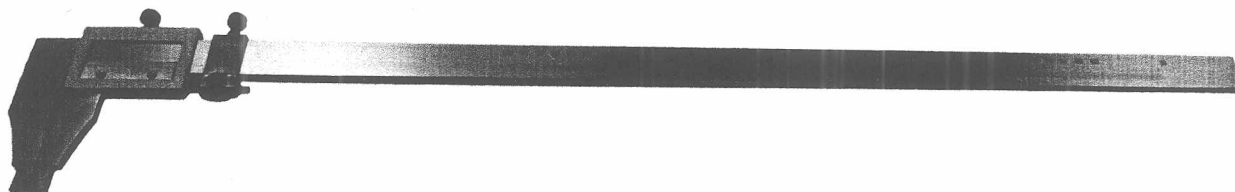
Внешний вид штангенциркуля типа ШЦ-III
